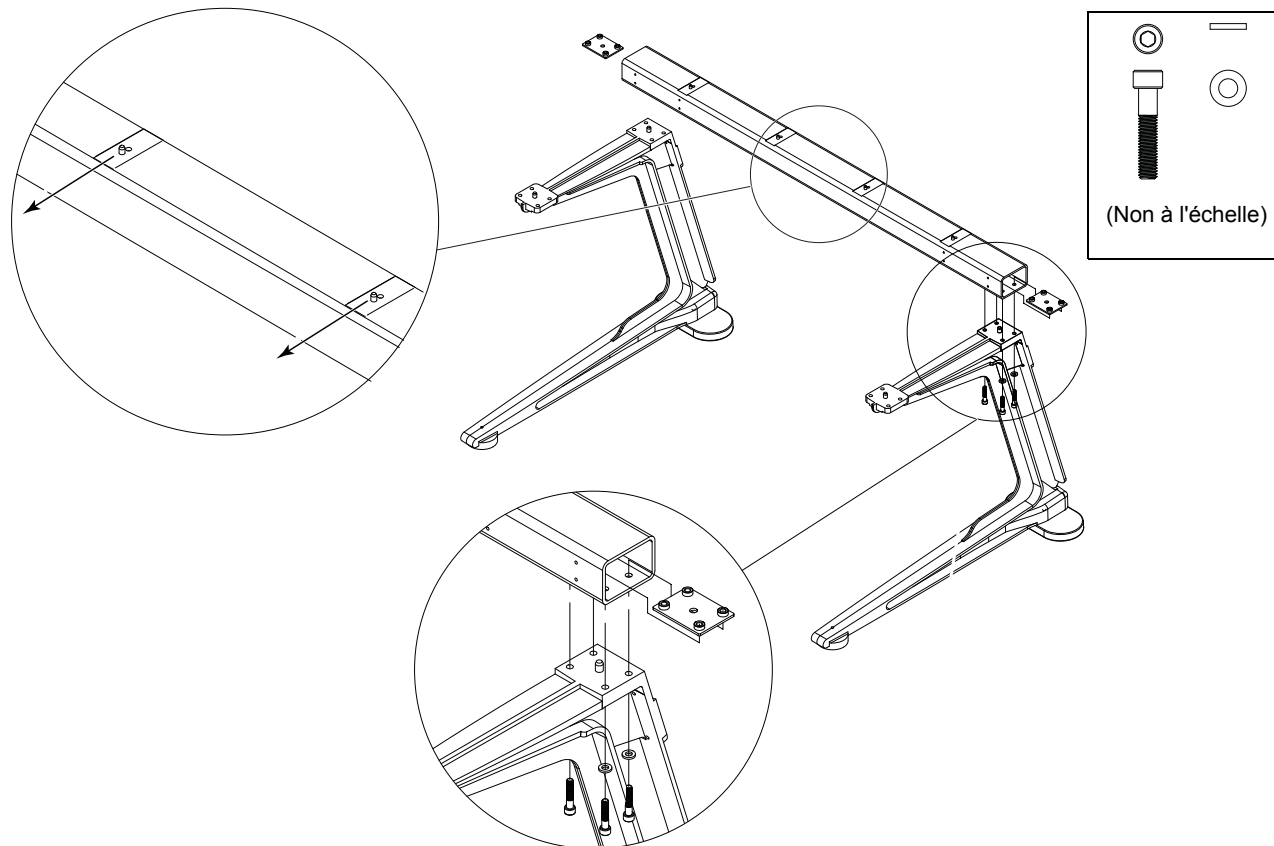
Fixation d'une entretoise sur les pieds à l'aide d'une plaque de montage d'entretoise
